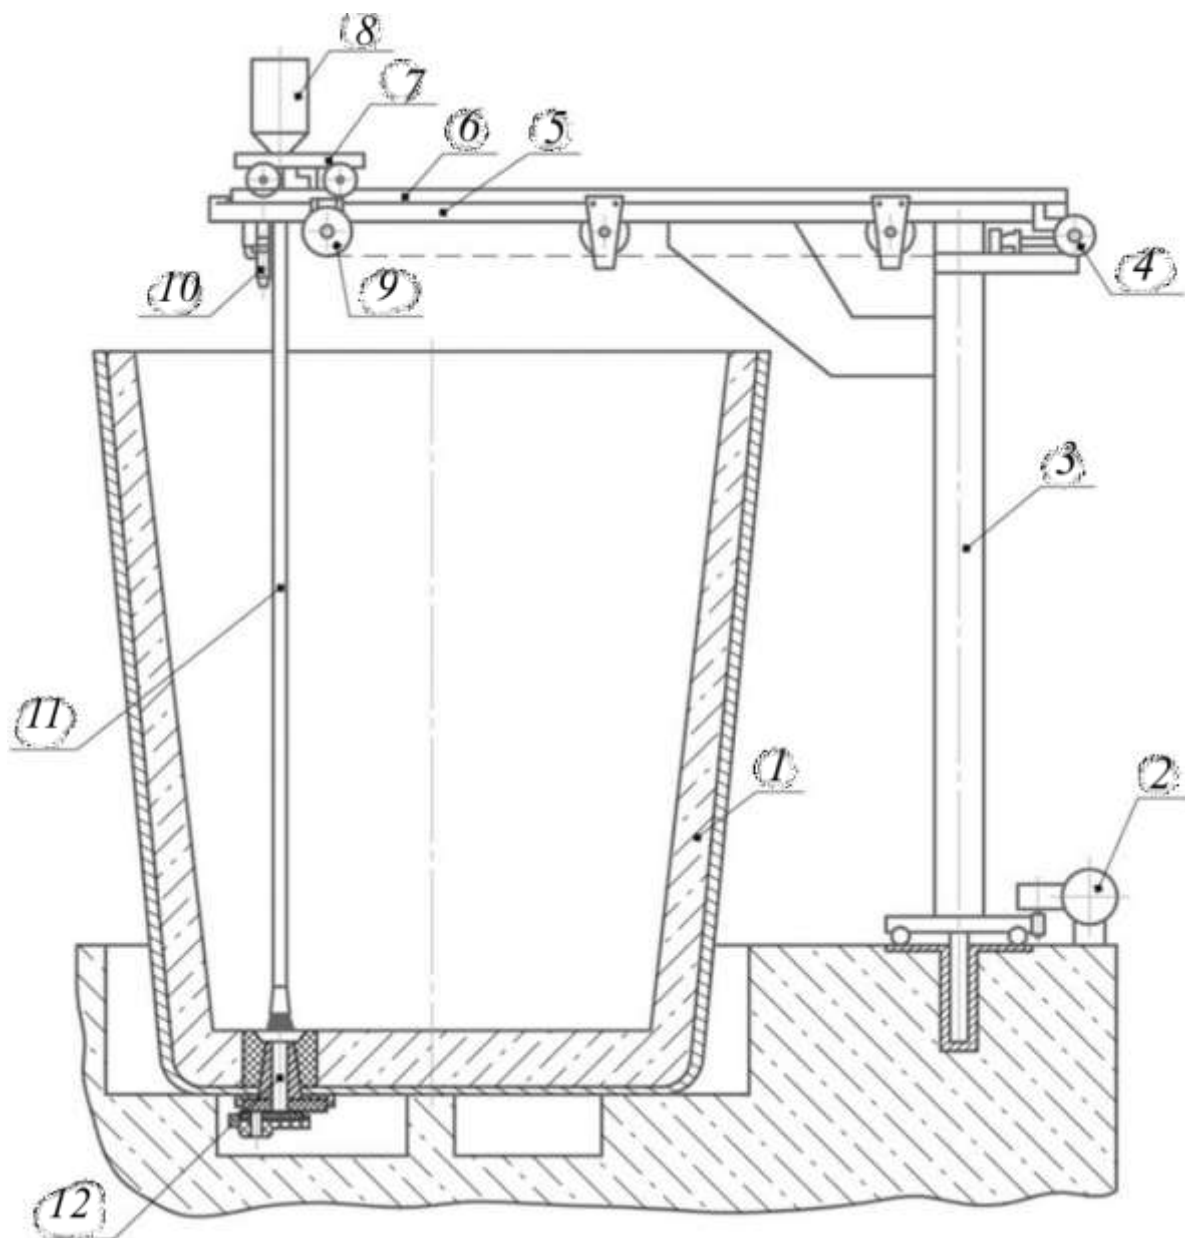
Положение манипулятора для механизированной подачи стартовой смеси во время ее высыпания самотеком из питающего бункера в выпускной канал сталеразливочного ковша: 1 – ковш, 2 – привод вращения колонны, 3 – колонна, 4 – ведущая звездочка, 5 – балки, 6 – направляющие, 7 – тележка, 8 – бункер, 9 – ведомая звездочка, 10 – лазерный визир-дальномер, 11 – металлический рукав, 12 – выпускной канал
